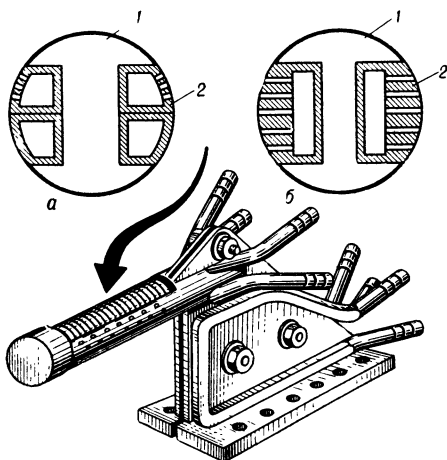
Петлевой индуктор для заделки внутренних цилиндрич. поверхностей способом одновременного нагрева при вращении закаливаемой детали: а — конструкция с отдельными камерами для охлаждения индуктора и выхода закалочной воды; б — конструкция без постоянного охлаждения; 1 — магнитопровод; 2 — индуктирующий провод.
